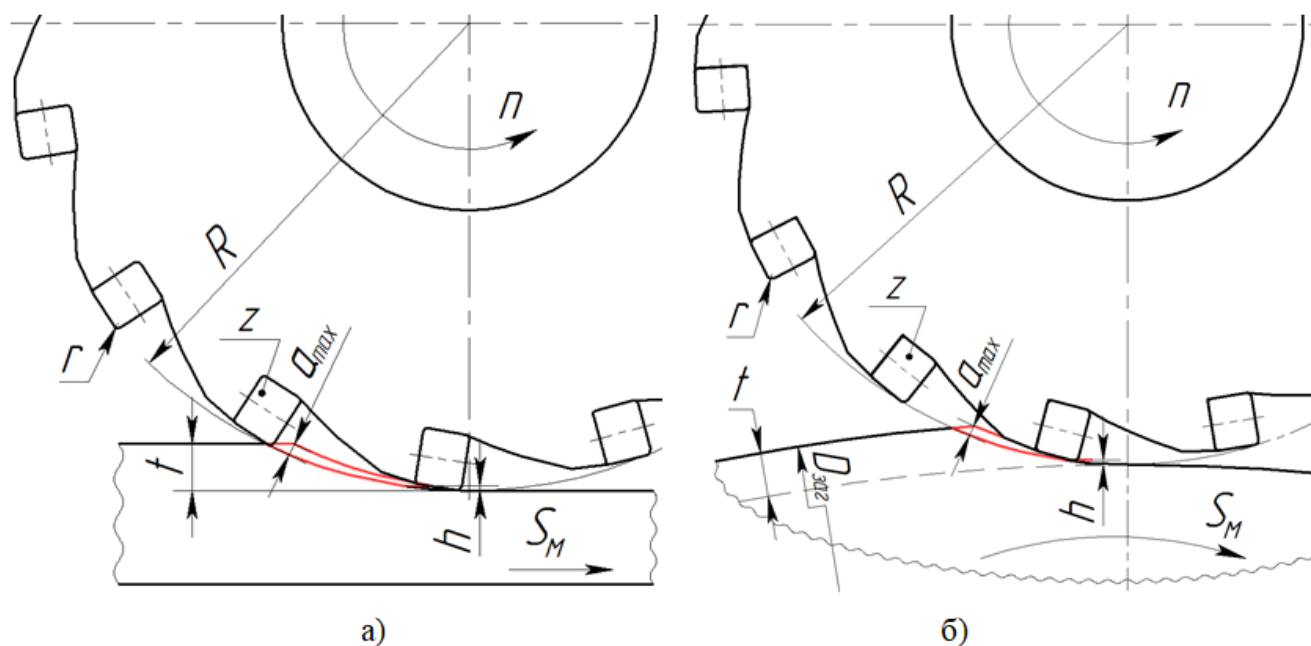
Схемы попутного фрезерования: прямолинейных направляющих (а) и деталей типа тела вращения (б), где S_M – подача заготовки; n – частота вращения фрезы; t – глубина резания; a_{max} – максимальная толщина стружки; R – радиус фрезы; z – количество режущих пластин; r – радиус округления режущих кромок СМП, h – глубина смятия материала заготовки ($h = r$).
